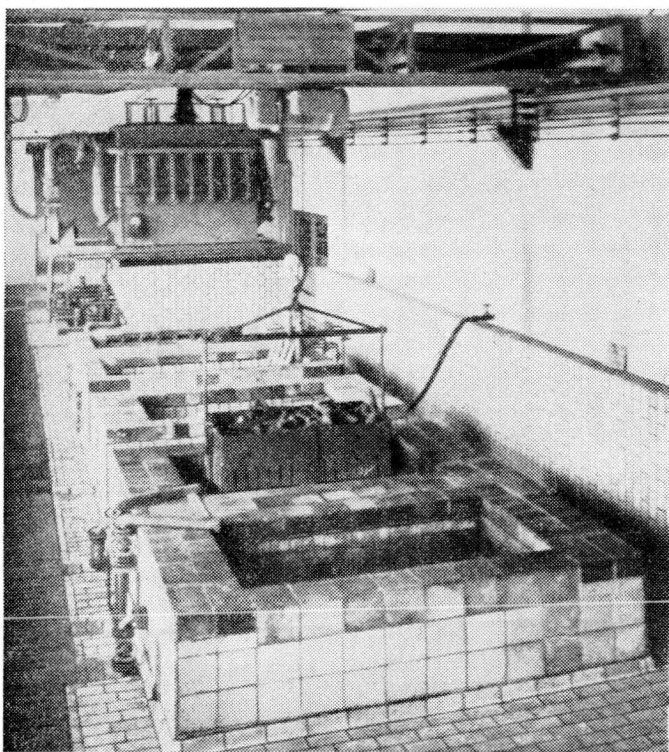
Instalação de decapagem para peças forjadas, composto de: tanques com exaustor na beirada e ar soprado; 2 tanques de decapagem; tanque de lavagem a quente e a frio; tanque de neutralização. Tôdas as partes visíveis são de ferro protegido por pinturas anticorrosivas. Paredes e assoalho feitos de tijolos anti-ácidos; a fábrica inclui também um regenerador de ácido sulfúrico, um neutralizador contínuo para águas usadas e tanque para armazenamento de ácido sulfúrico (Steuler — Industrierwerke, Hohn-Grenzhäusen perto Koblenz; Alemanha).
